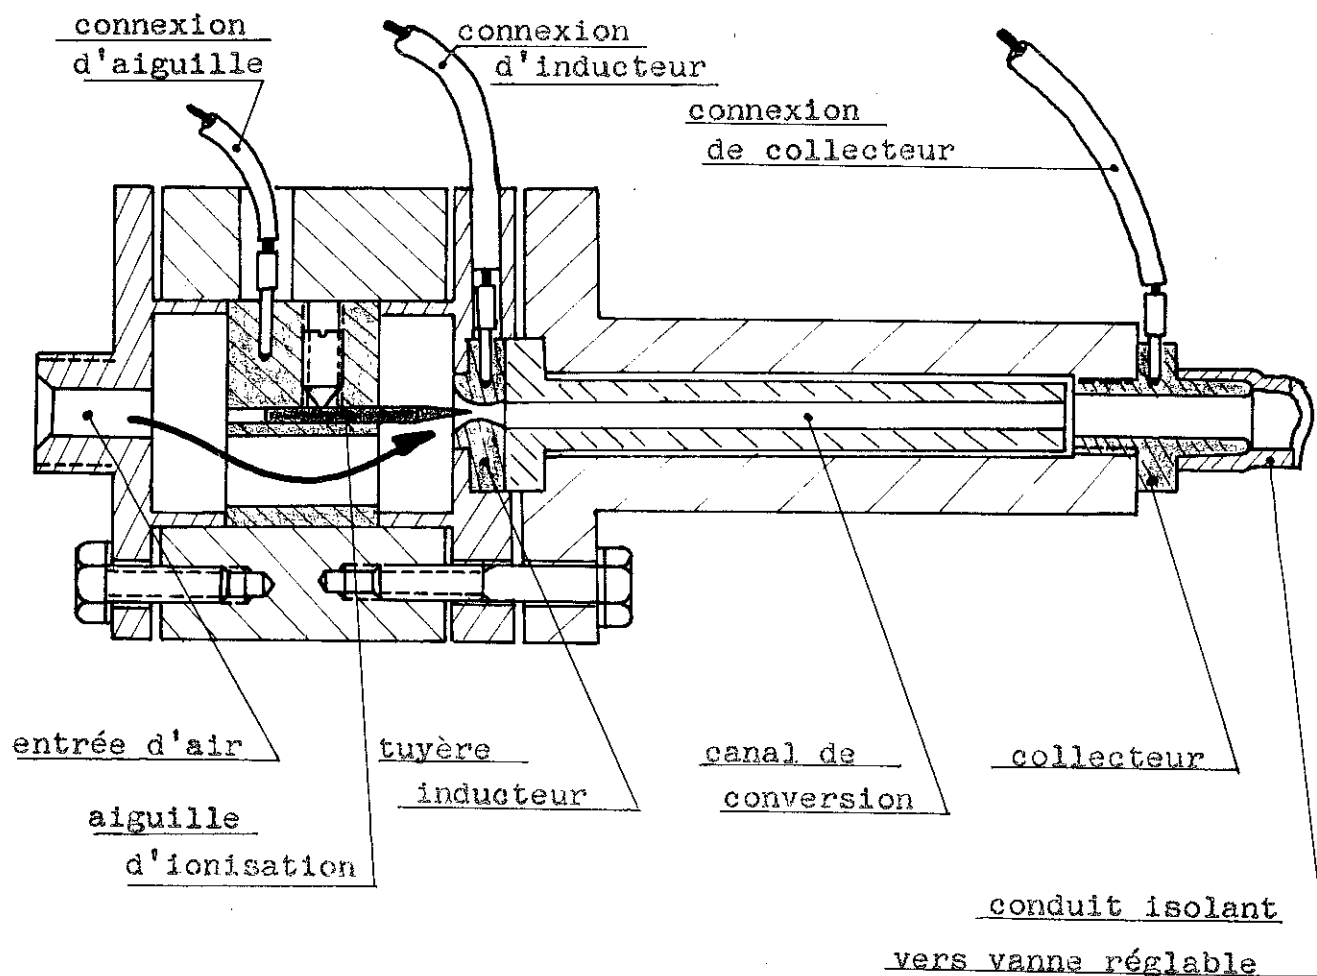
CONVERTISSEUR POUR ESSAIS PRELIMINAIRES
